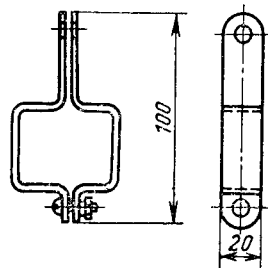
Хомут K544 для подвешивания осветительного шинпровода ШОС-67 на струнах и крепления его на корпусе распределительного шинпровода ШРА64.
